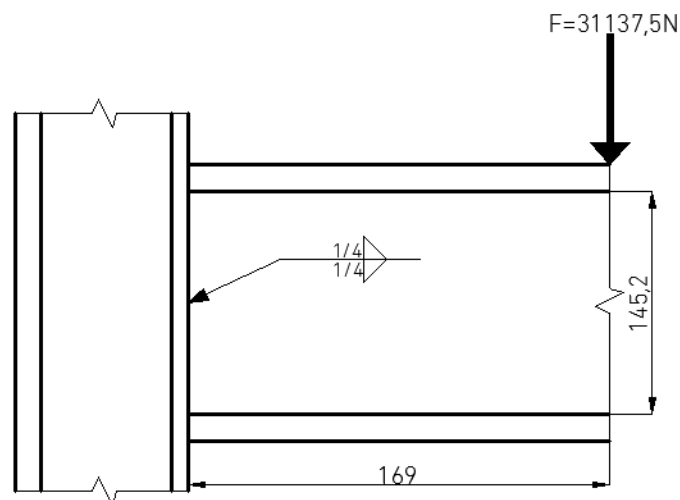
Unión Soldada de los perfiles ⁴⁵
